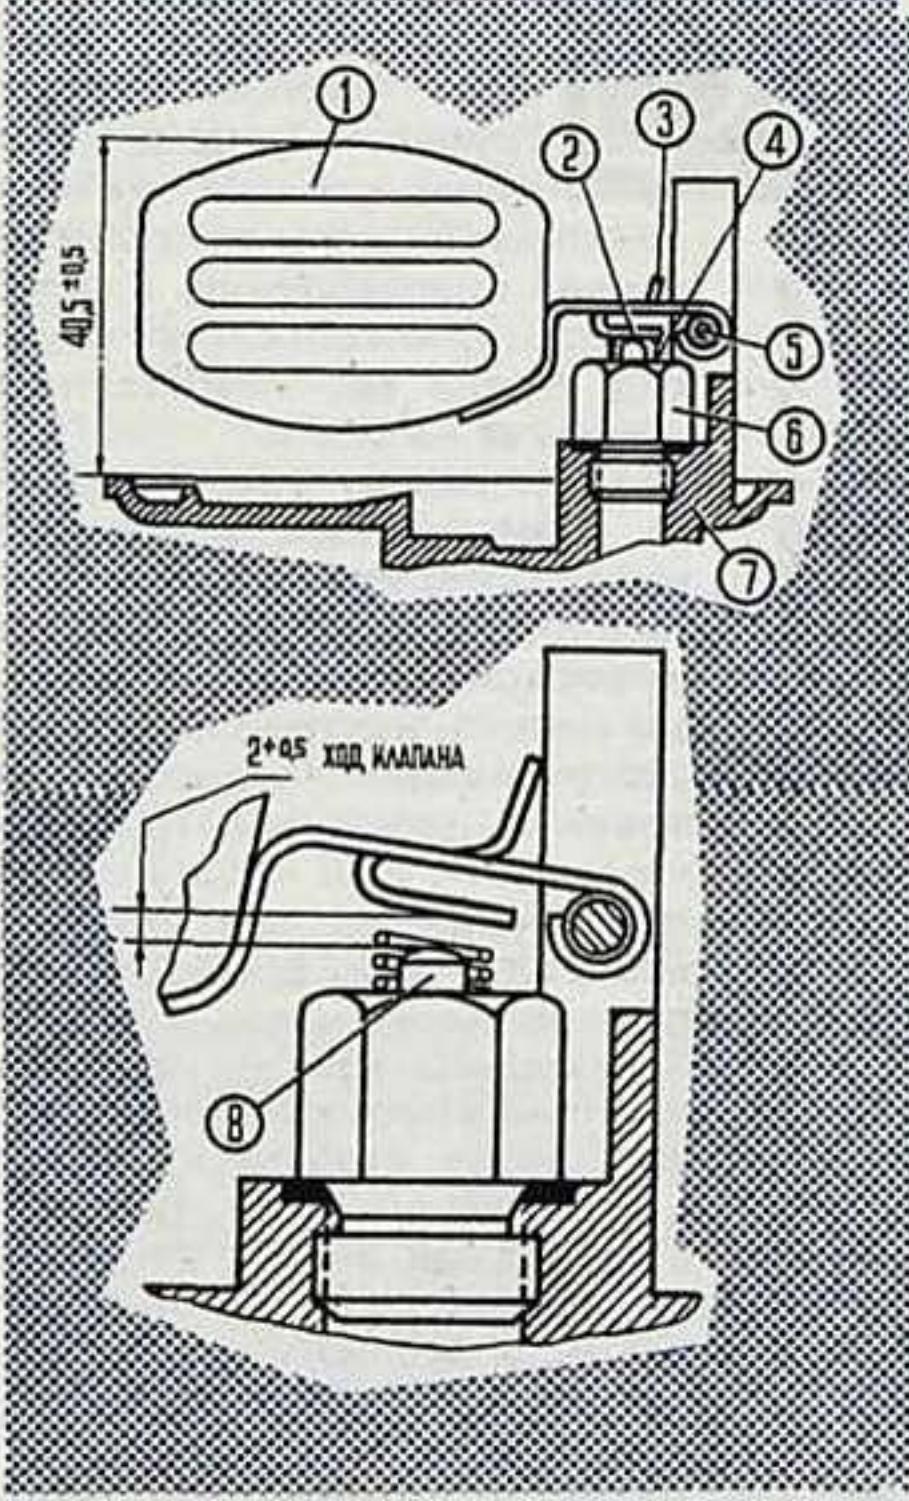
Поплавок: 1 — поплавок; 2 — язычок для установки уровня; 3 — ограничитель хода поплавка; 4 — пружина; 5 — ось поплавка; 6 — корпус клапана подачи топлива; 7 — крышка карбюратора; 8 — игла клапана подачи топлива.
